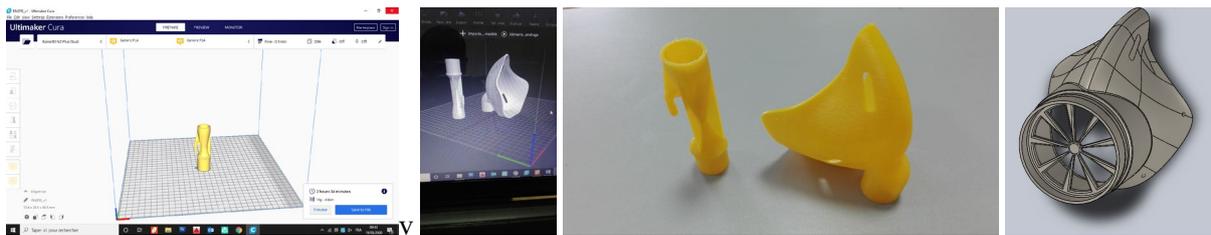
Valve de venturi 1 imprimée en 3D - Dessin de Lassad AKERMI (Génie Mécatronique) à partir du fichier OpenSource trouvé par l'équipe. 2. Valve de Venturi + Casque imprimés en 3D - Dessin de Lassad AKERMI (Génie Mécatronique) à partir du fichier OpenSource trouvé par l'équipe. 3. Valve de Venturi + Casque imprimés en 3D. 4. Masque N95 Modélisé par Lassad AKERMI (ENICarthage).
